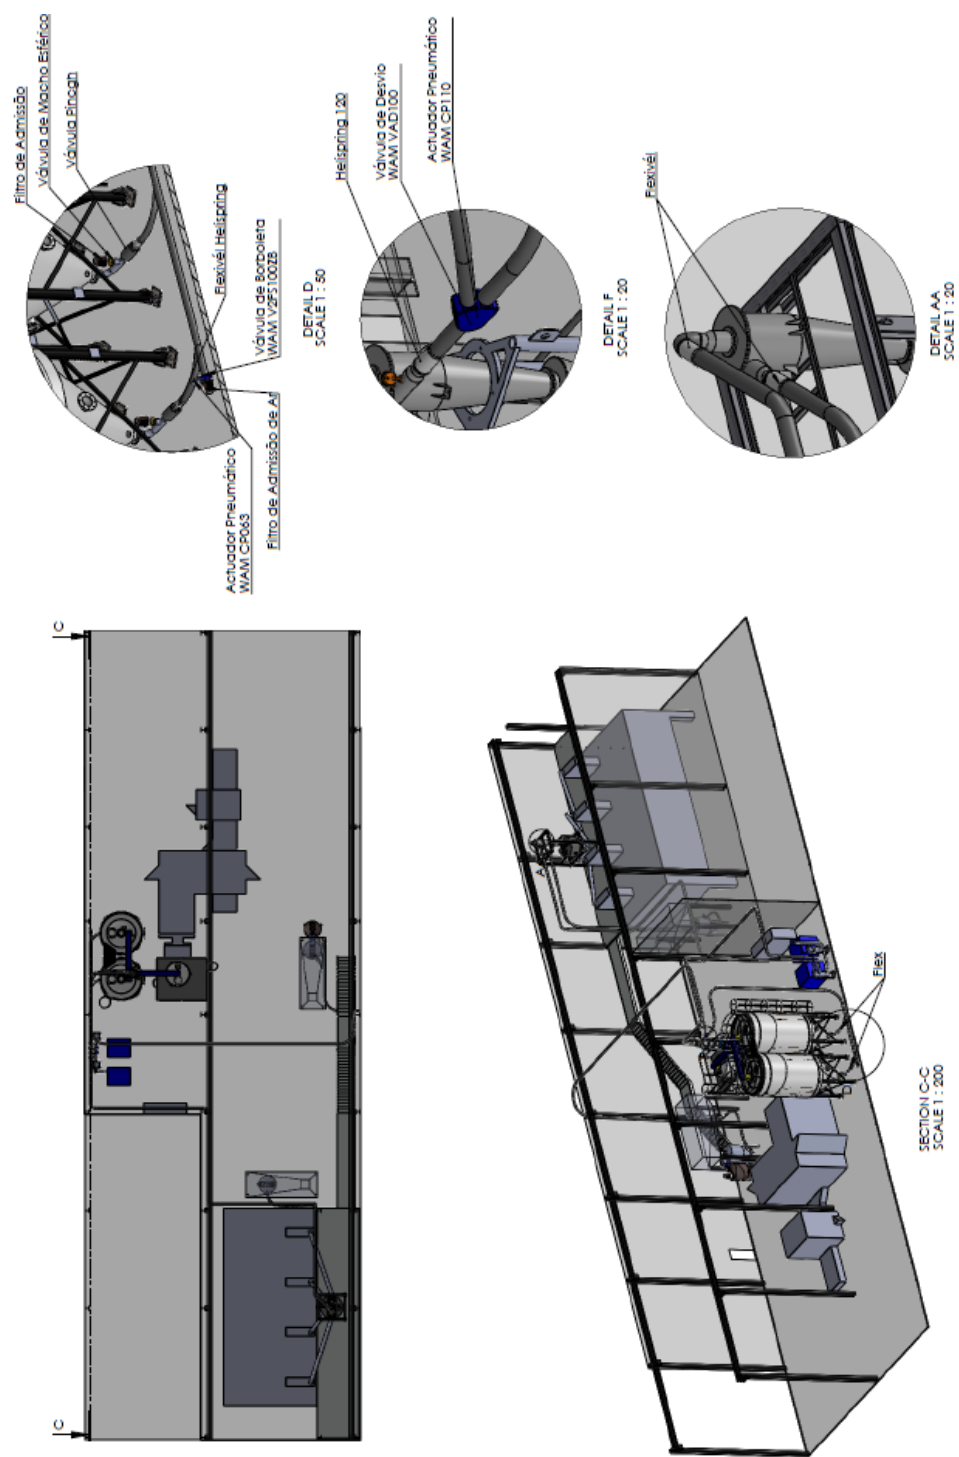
Layout fabril com representação do traçado da tubagem-2.
